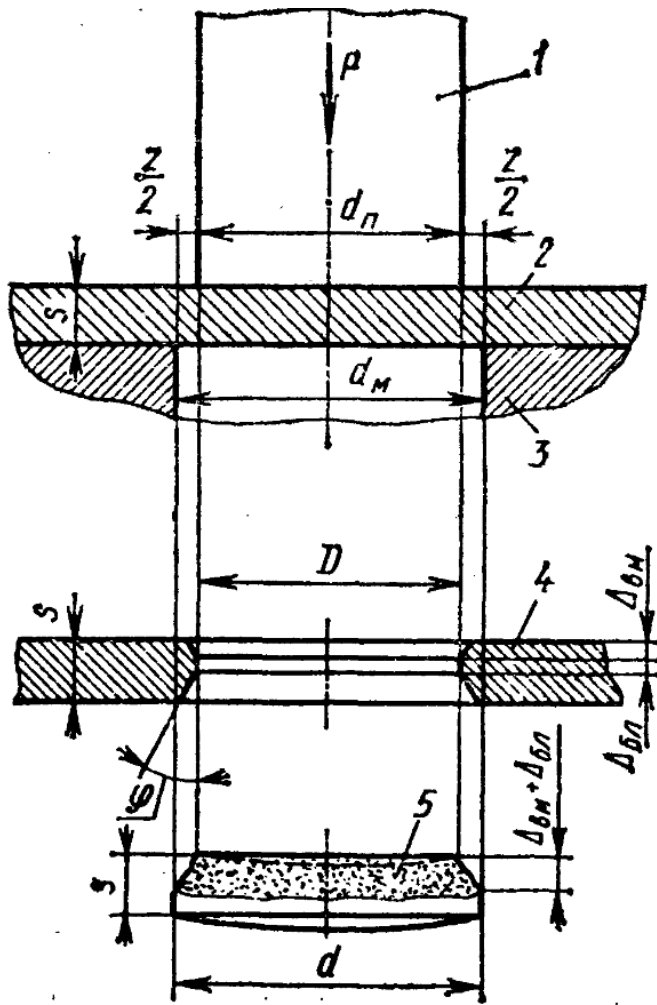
Схема пробивки-вырубki и погрешности деталей после штамповки: 1 – пуансон; 2 – заготовка; 3 – матрица; 4 – заготовка с пробитым отверстием; 5 – вырубленная деталь ($\Delta_{вм}$ – глубина вмятины, образующейся в начальный момент пробивки-вырубki; $\Delta_{бл}$ – высота блестящего пояска; φ – угол скола).
